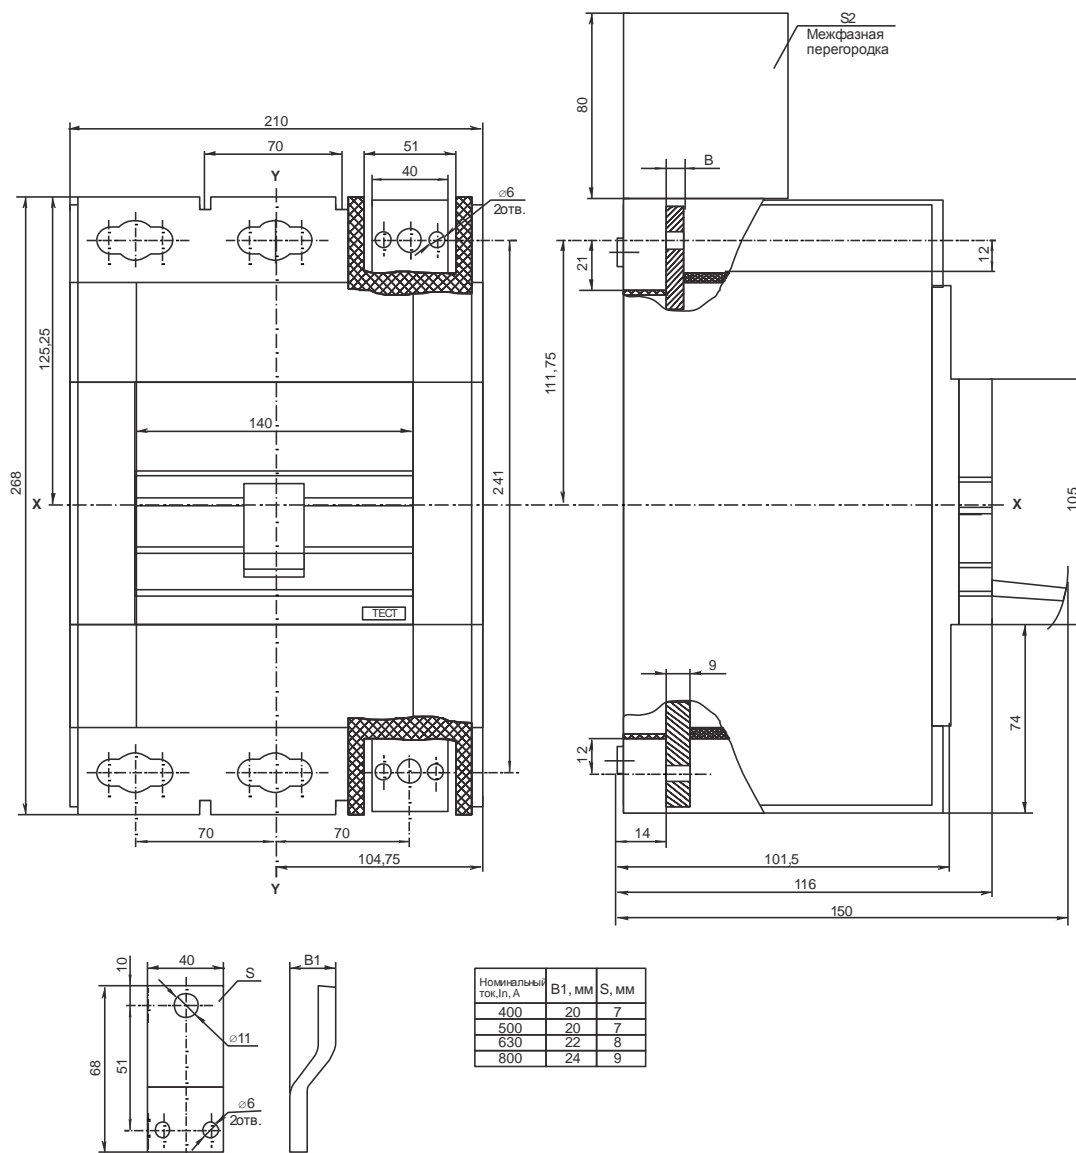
Габаритные и установочные размеры выключателя ВА88-35
